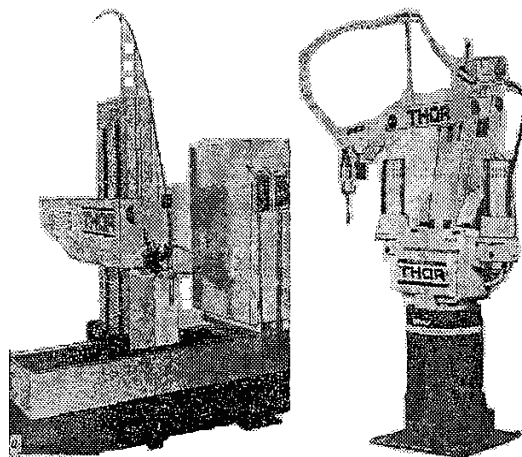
Роботи для зварювання фірми «Осака трансформер» (Японія)
